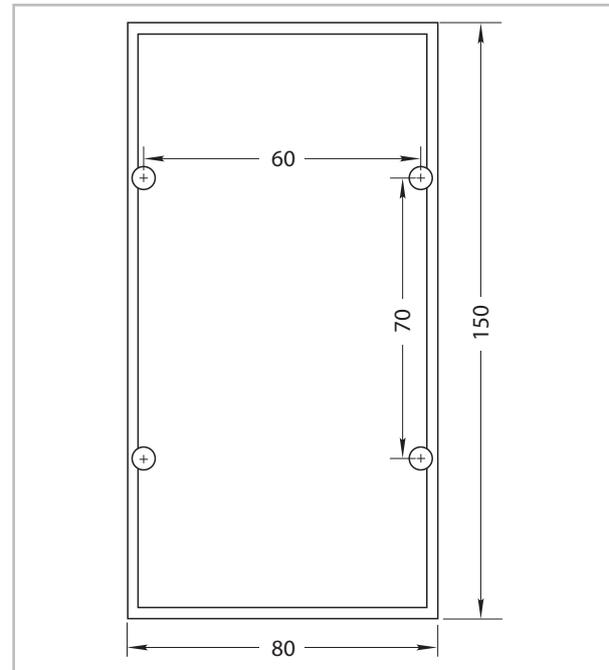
Aufbau und Maße des Wandhalters (Alle Angaben in mm)
